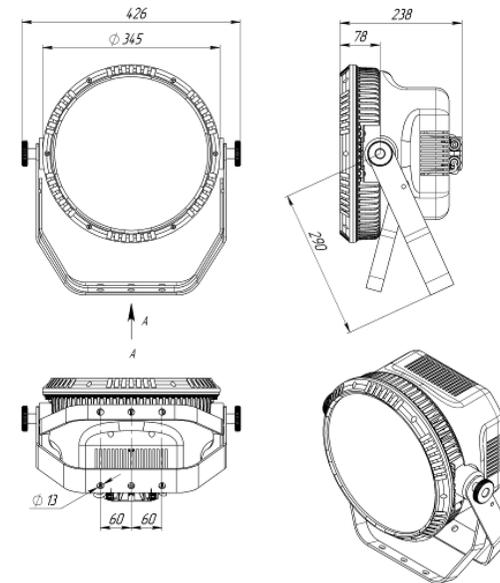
Габаритные размеры светильника «L-banner 600»
